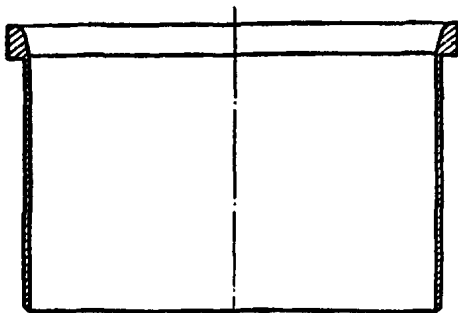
Приспособление для установки подвижного контакта камеры в корпус
